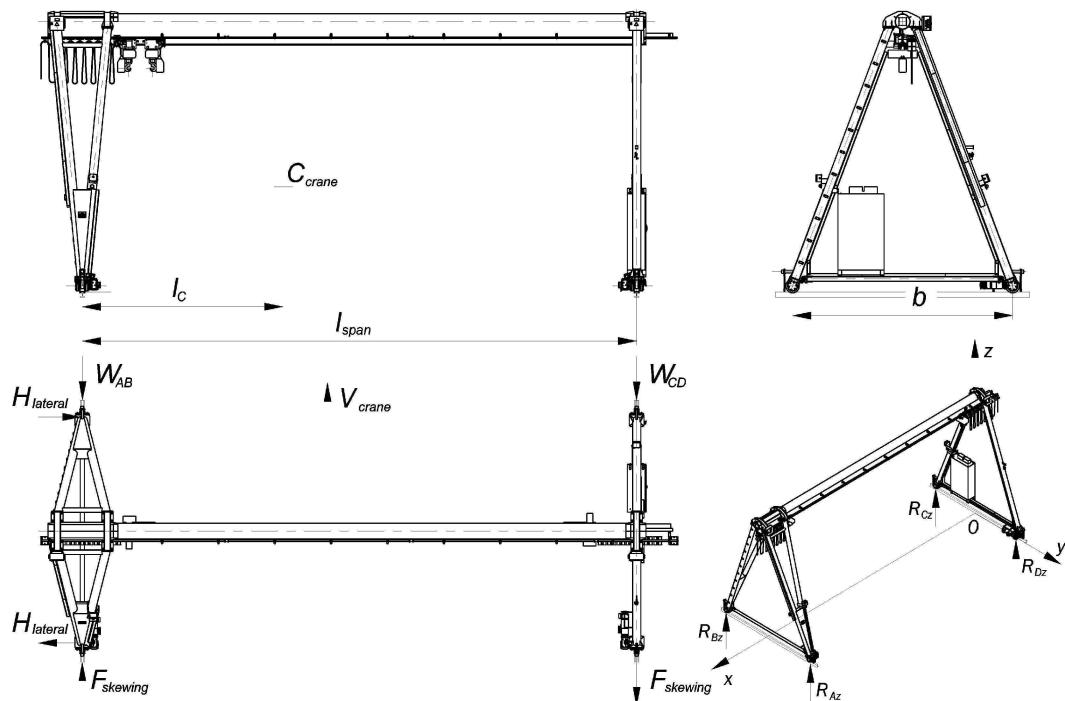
Общий вид козлового крана с расчетной схемой нагрузок при перекосе
